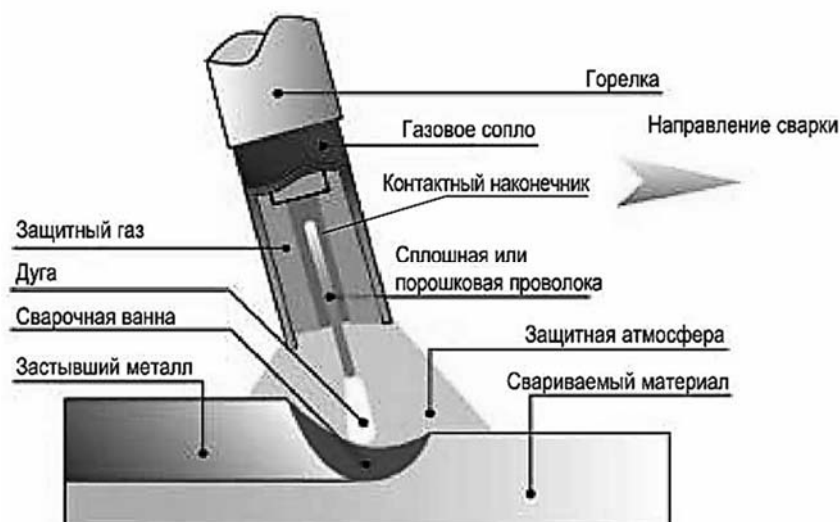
Схема процесса сварки в защитных газах плавящимся электродом
